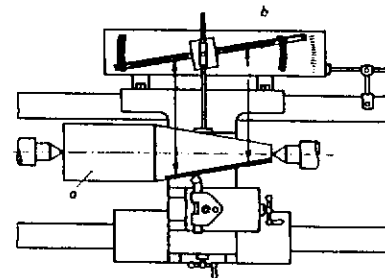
Torneado cónico con regla de guía. a) Pieza a tornear; b) regla de guía.
